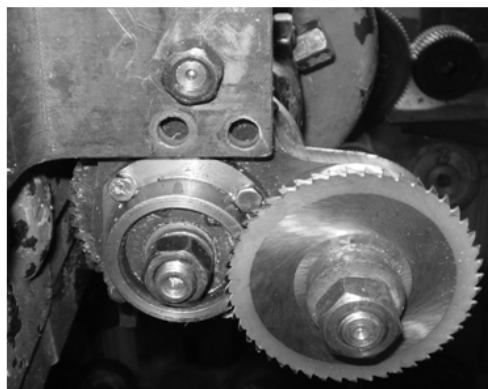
Нарізання глобоїдного черв'ячного колеса дисковою фрезою на зубофрезерному верстаті з мультиплікатором та зі зміною закону формоутворення
